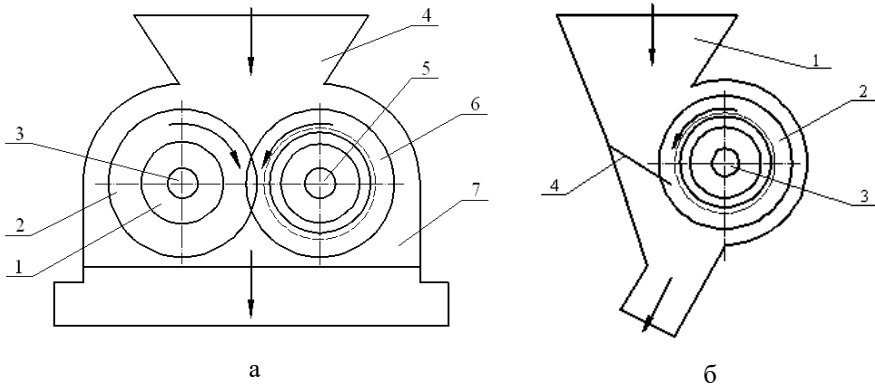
Схеми багатодискових різальних машин: а) саморізка для подрібнення жиру сирцю: 1 – проміжна шайба; 2 – дискові ножі; 3, 5 – вали; 4 – завантажувальний бункер; 6 – барабан; 7 – корпус; б) багатодискова м'ясорізка: 1 – корпус; 2 – дискові ножі; 3 – вал; 4 – гребінець
